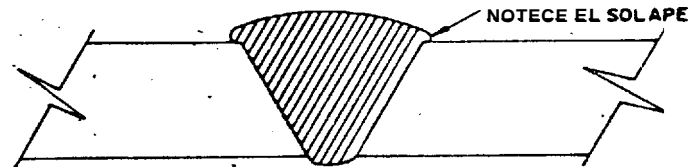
CONDICION DE SOLAPE (REF. AWS WELDING HANDBOOK) (Ref. 7)
